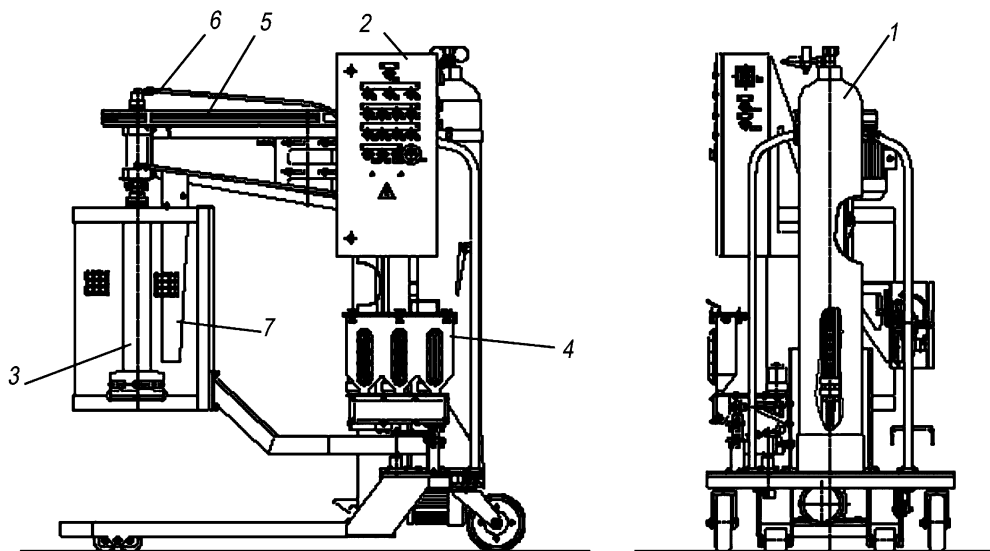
Схема установки продувки расплава П1873.00.000: 1 – баллон инертного газа; 2 – пульт управления; 3 – импеллер; 4 – бункер для загрузки флюса; 5 – привод вращения; 6 – трубопровод подачи газа; 7 – рассекатель
